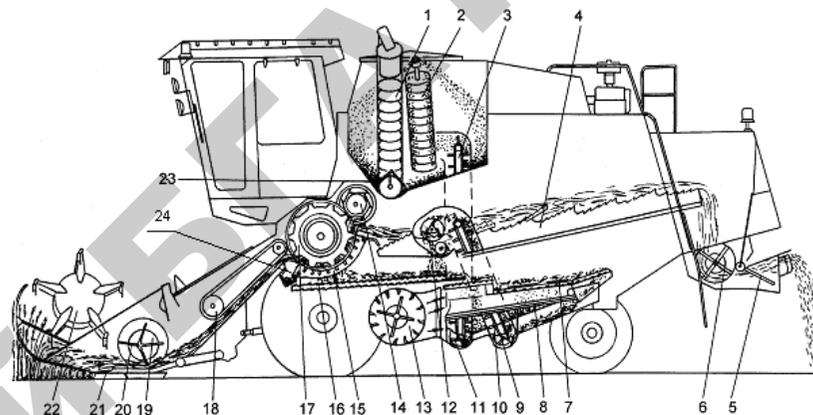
Схема технологического процесса комбайна: 1 — шнек поворотный выгрузной; 2 — шнек загрузной зерновой; 3 — элеватор зерновой; 4 — соломотряс; 5 — дефлектор; 6 — соломоизмельчитель; 7 — верхний решетный стан; 8 — нижний решетный стан; 9 — шнек колосовой; 10 — элеватор колосовой; 11 — шнек зерновой; 12 — устройство домолачивающее; 13 — вентилятор; 14 — битек отбойный; 15 — подбарабанье; 16 — транспортная (стрясная) доска; 17 — барабан молотильный; 18 — транспортер наклонной камеры; 19 — шнек; 20 — механизм пальчиковый; 21 — аппарат режущий; 22 — мотовило; 23 — шнек горизонтальный; 24 — камнеуловитель
